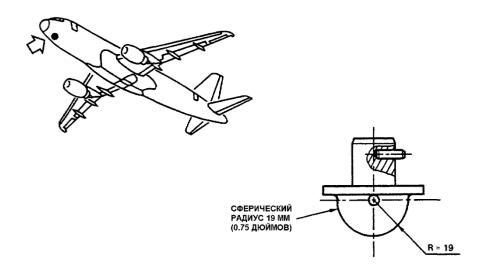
Нагрузки на точки опор гидроподъёмников воздушного судна Точка опоры гидроподъёмника на крыло STA4067 (FR8) Модель 200 – Двухколесный
